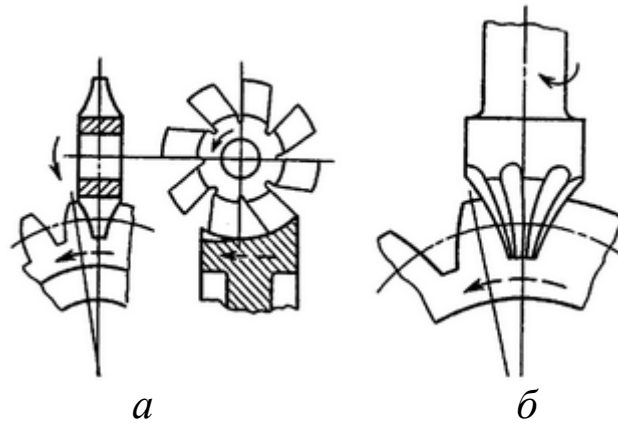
Схема нарезания зубчатых колес модульными фрезами:
